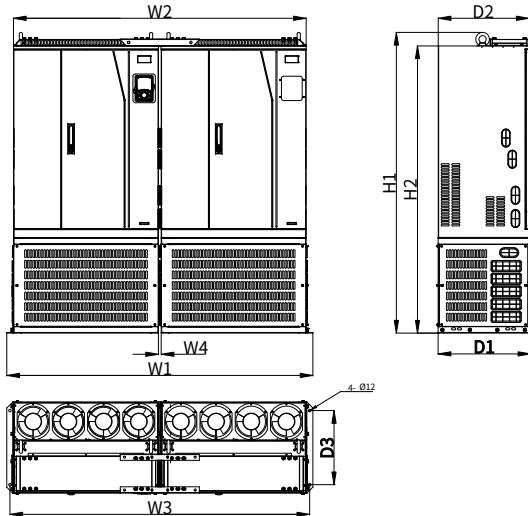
380V 710~3000kW 并机外形及安装尺寸
